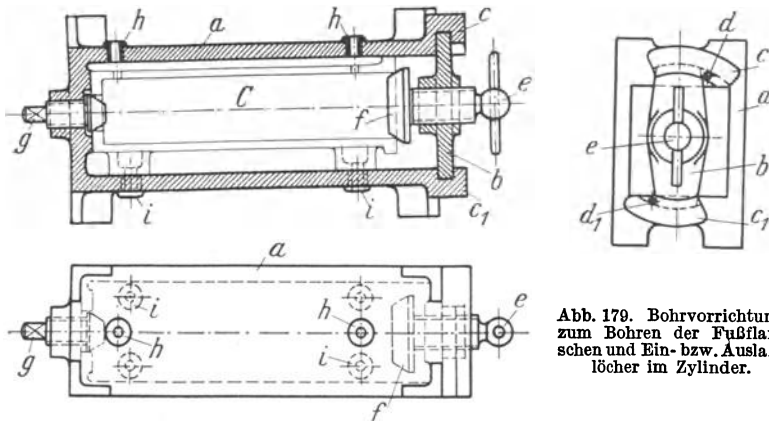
Bohrvorrichtung zum Bohren der Fußflanschen und Ein- bzw. Auslaßlöcher im Zylinder.
